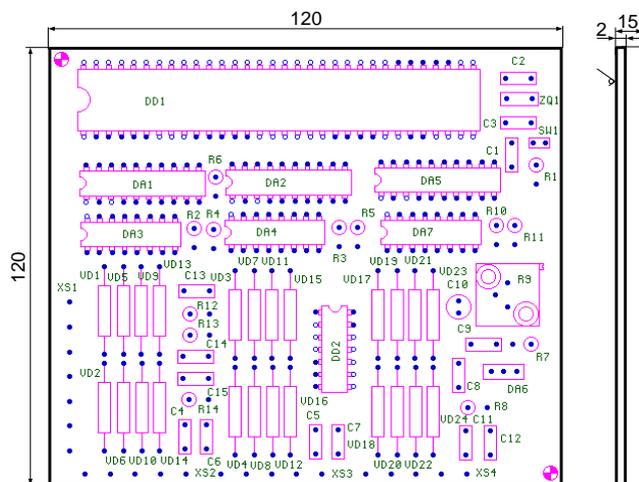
Сборочный чертеж печатной платы устройства позиционирования
